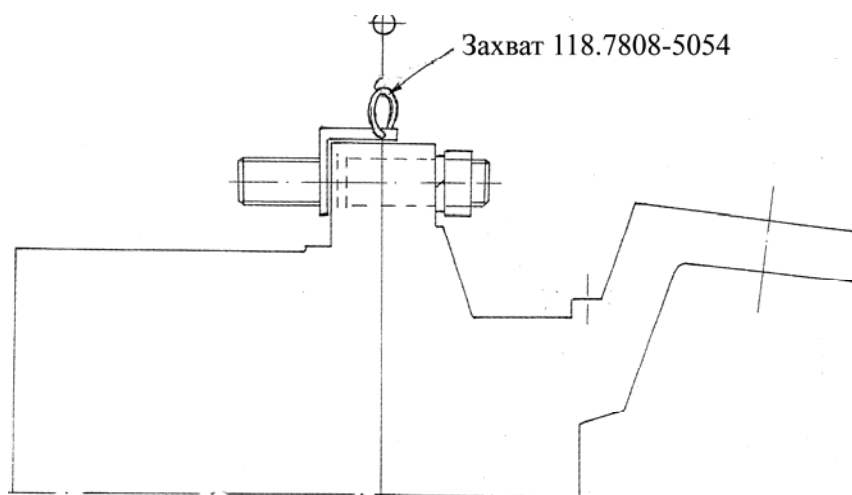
Схема строповки и индекс захвата колесного редуктора.
